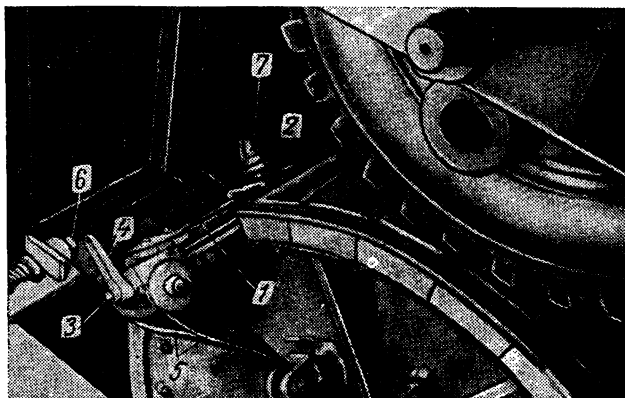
Барабан шинообкатного станка с механизмом передвижения препятствия:
